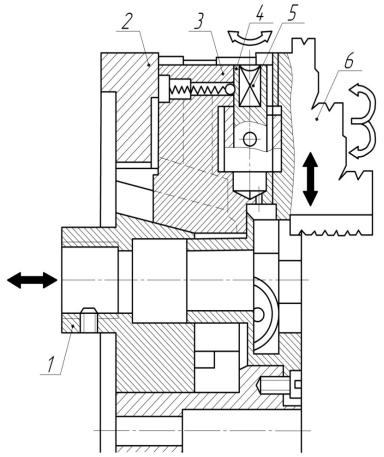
Самоцентрирующий трехкулачковый клиновой быстропереналаживаемый патрон с механизированным приводом: 1 — клиновая втулка; 2 — корпус; 3 — основание кулачка; 4 — шариковый фиксатор; 5 — винт; 6 — кулачок
